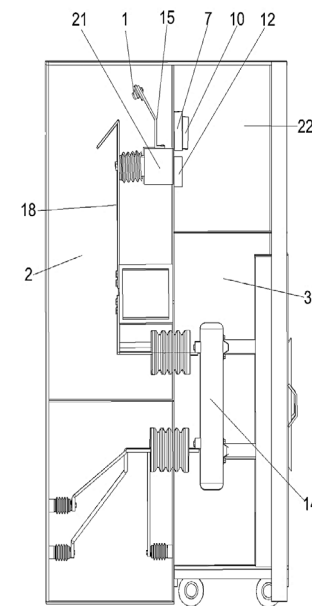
Расположение конструкции ресурсосберегающей релейной защиты внутри ячейки КРУ
